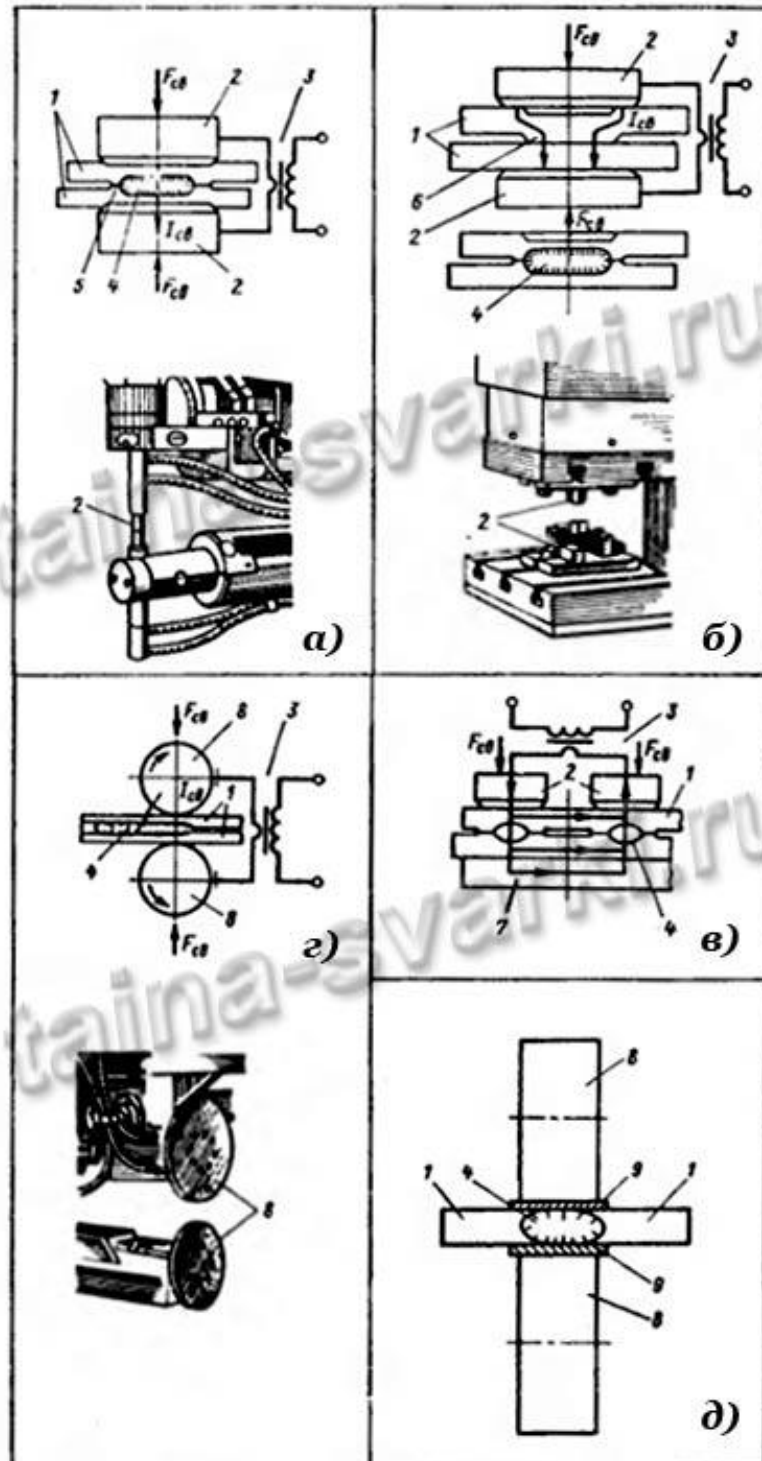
Схеми основних процесів контактного зварювання
